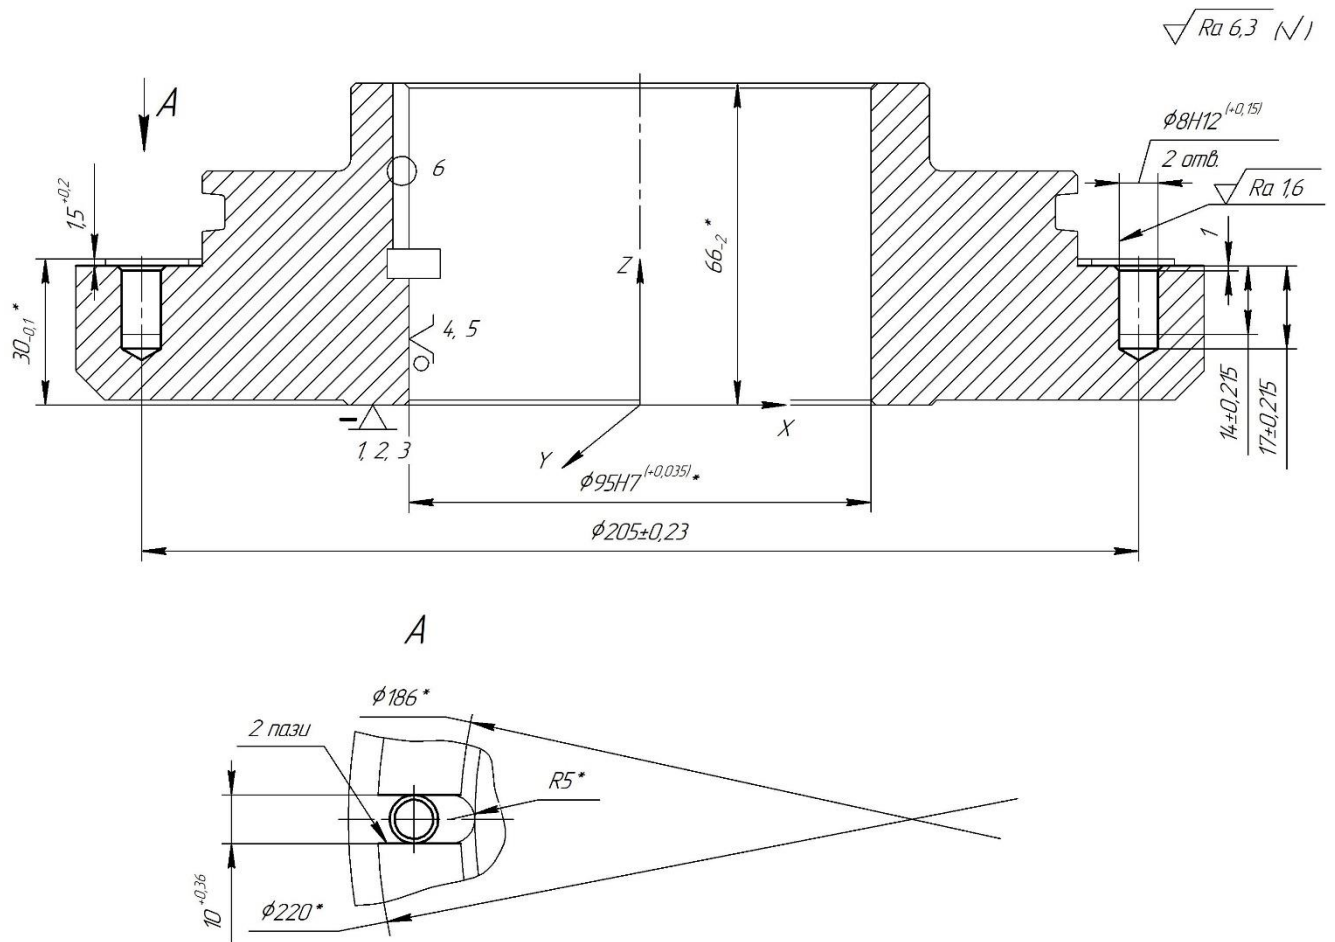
Схема базування і закріплення заготовки на операції комплексній на обробному центрі з ЧПК, установ А
